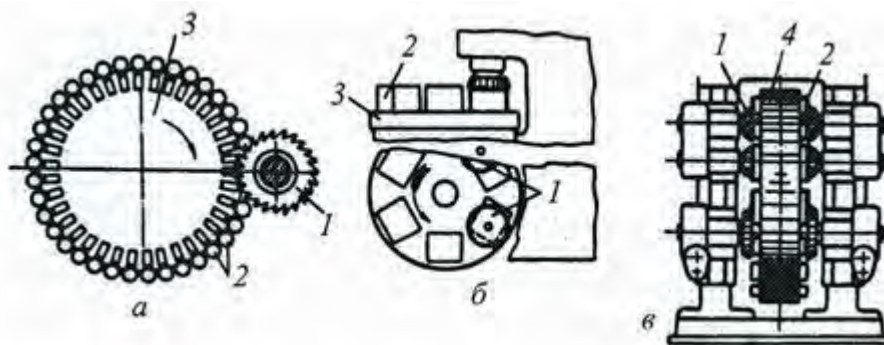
Фрезерування заготовок на фрезерних верстатах з безперервною круговою подачею
